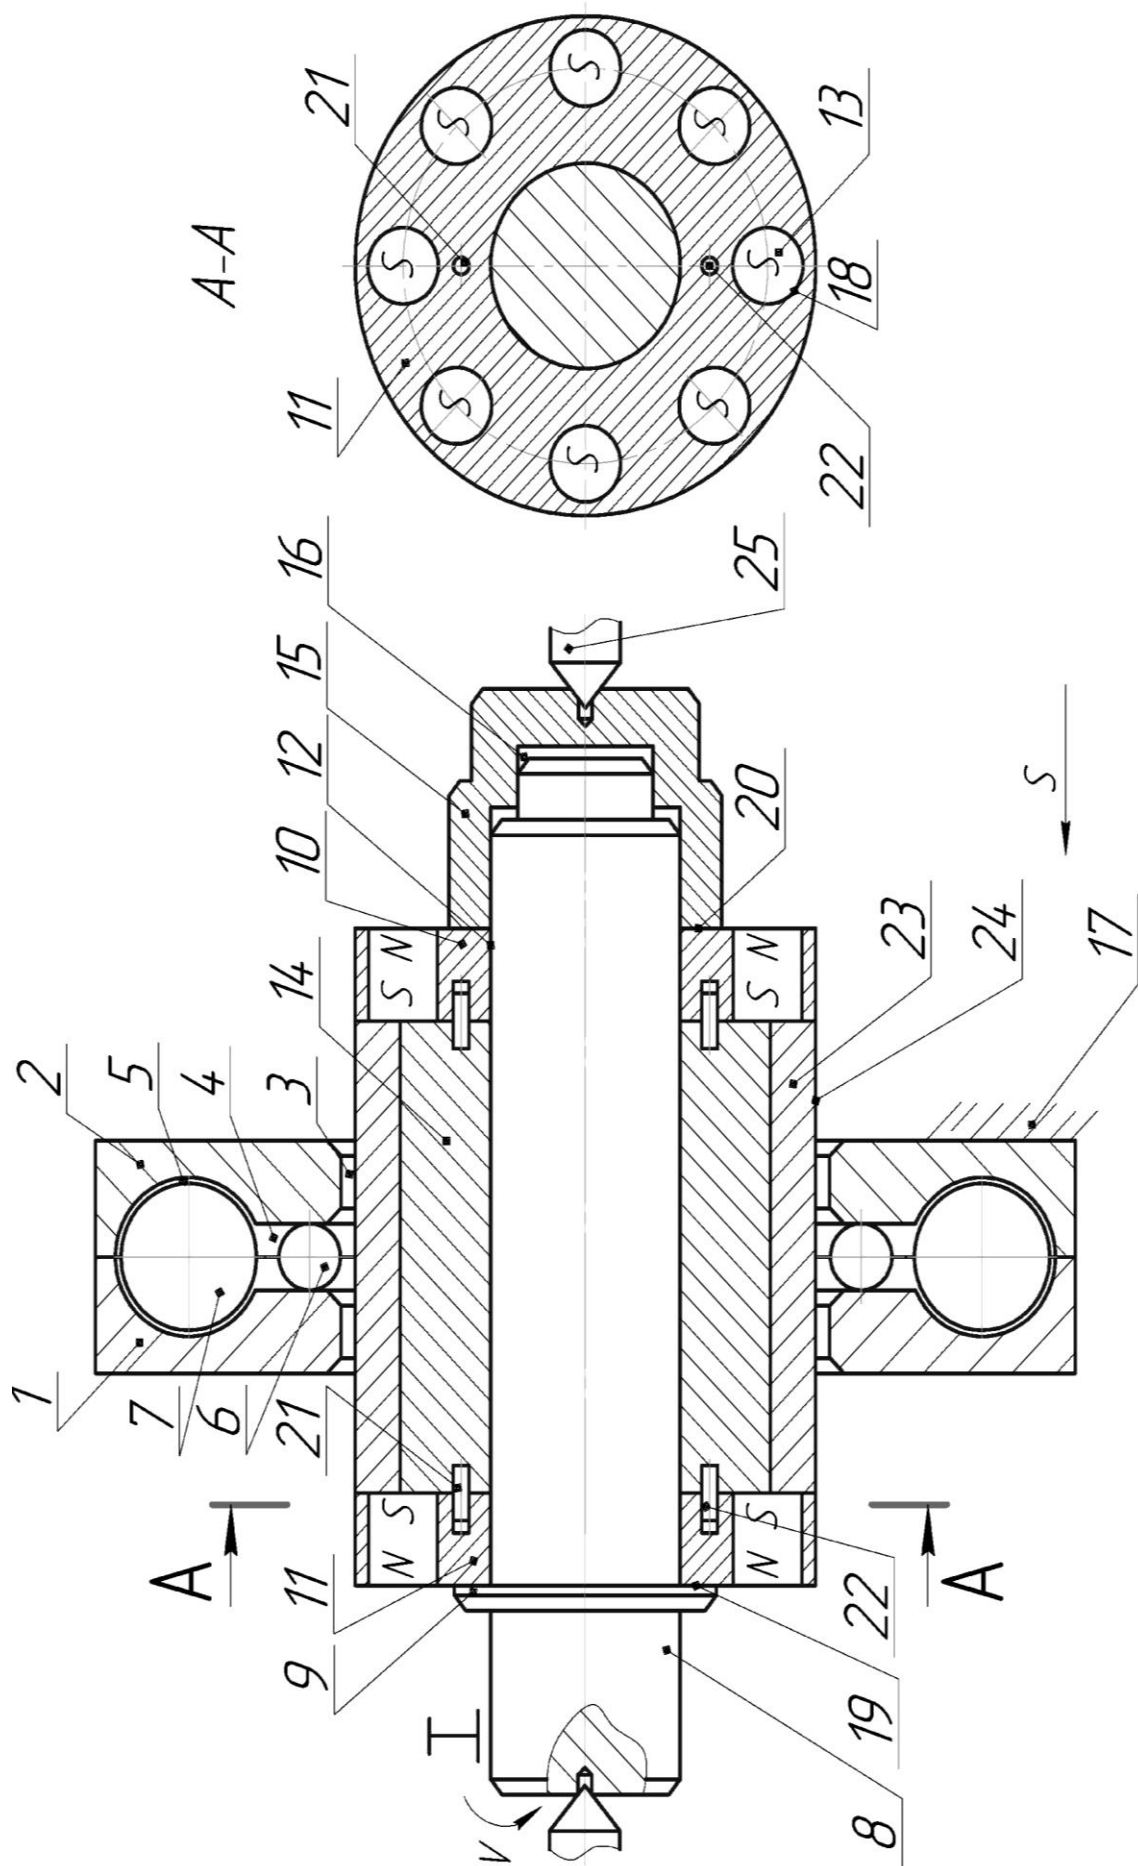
Конструкция устройства для магнитно-динамического упрочнения наружной поверхности втулок
